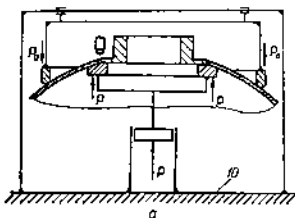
Принципиальные схемы приспособлений для сварки фланцев в сферические оболочки
